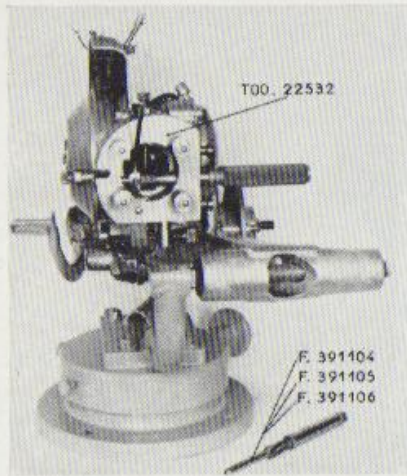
Coutil pour le réalésage de la bague du pied de bielle.
